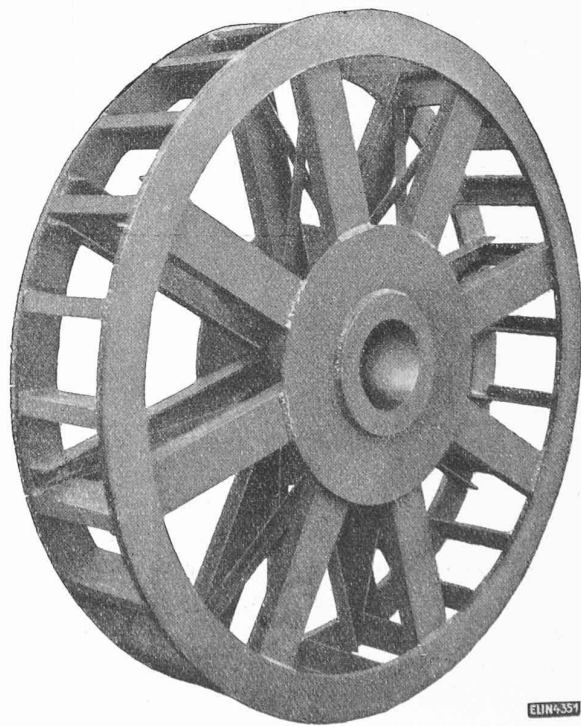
Rotor d'un moteur de 800 ch, construction Elin.
